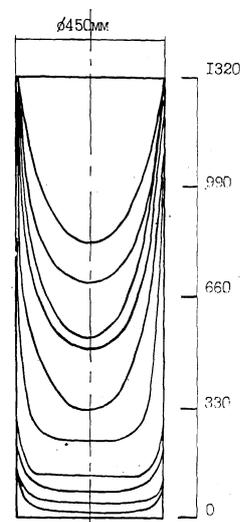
Изменение формы и глубины жидкой ванны металла в процессе наплавления слитка второго переплава
